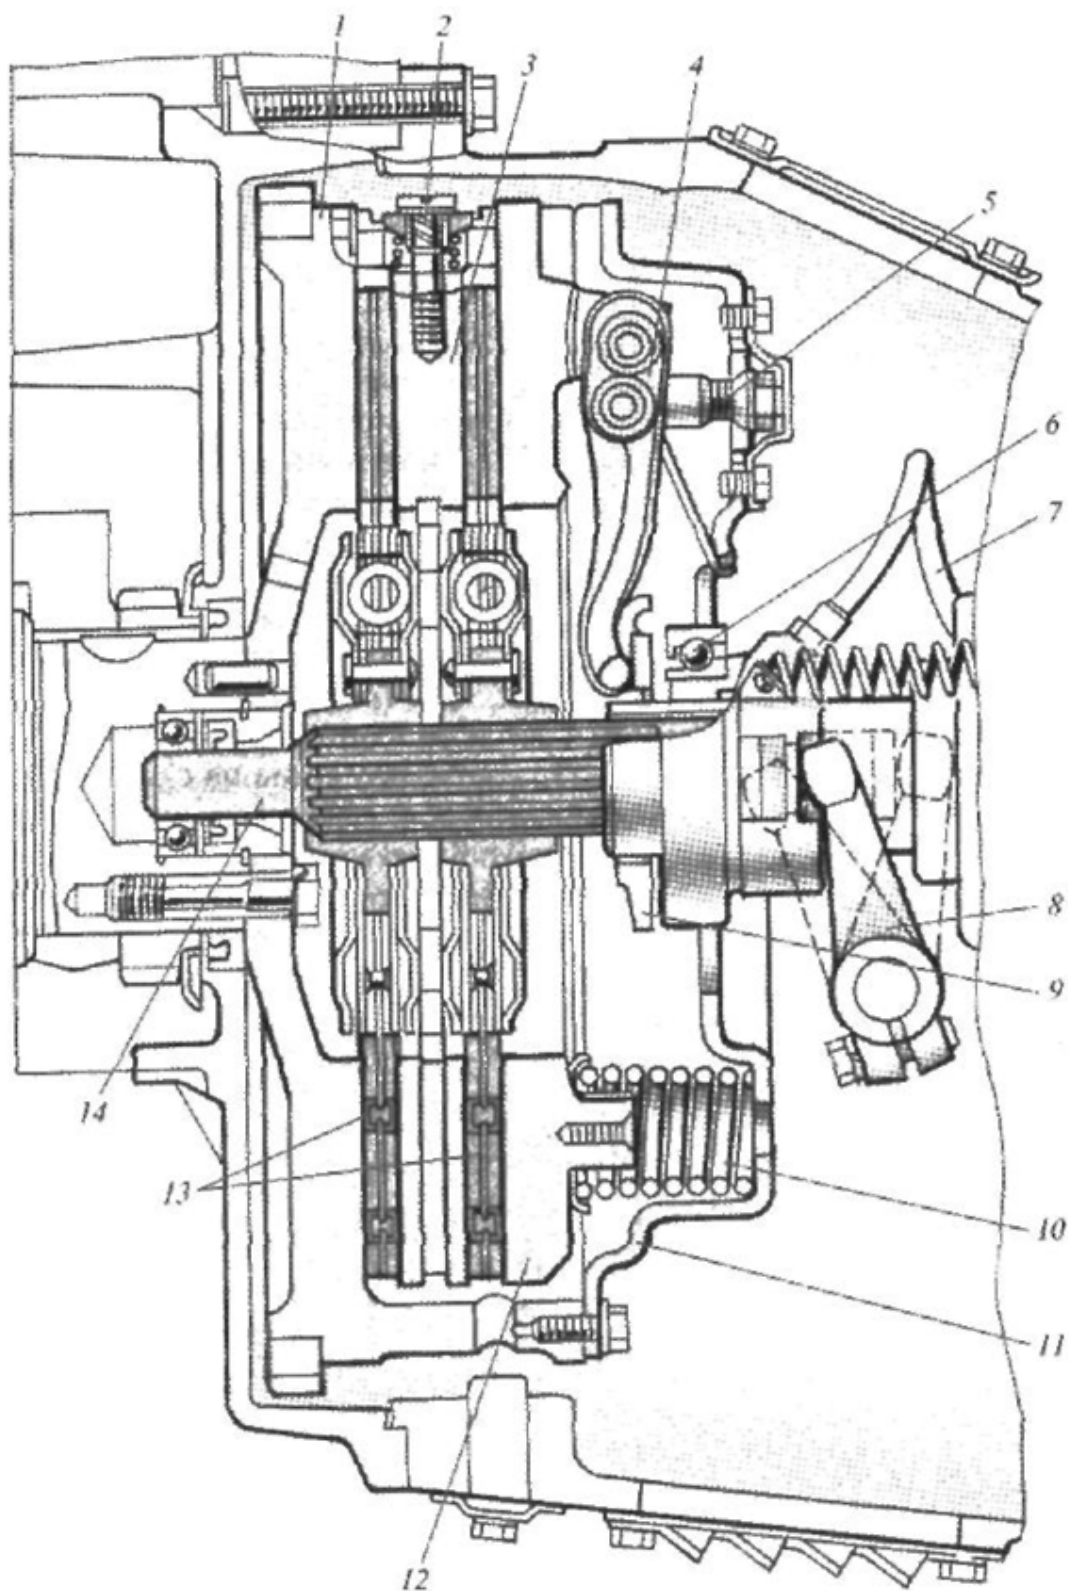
Двухдисковое постоянно-замкнутое сцепление: 1 - маховик; 2 - рычажной механизм; 3 - промежуточный диск; 4 - отжимной рычажок; 5 - вилка; 6 - упорный подшипник; 7 - шланг смазывания подшипника; 8 - вилка выключения; 9 - упорное кольцо; 10 - нажимная пружина; 11 - кожух; 12 - нажимной диск; 13 - ведомые диски; 14 - вал
